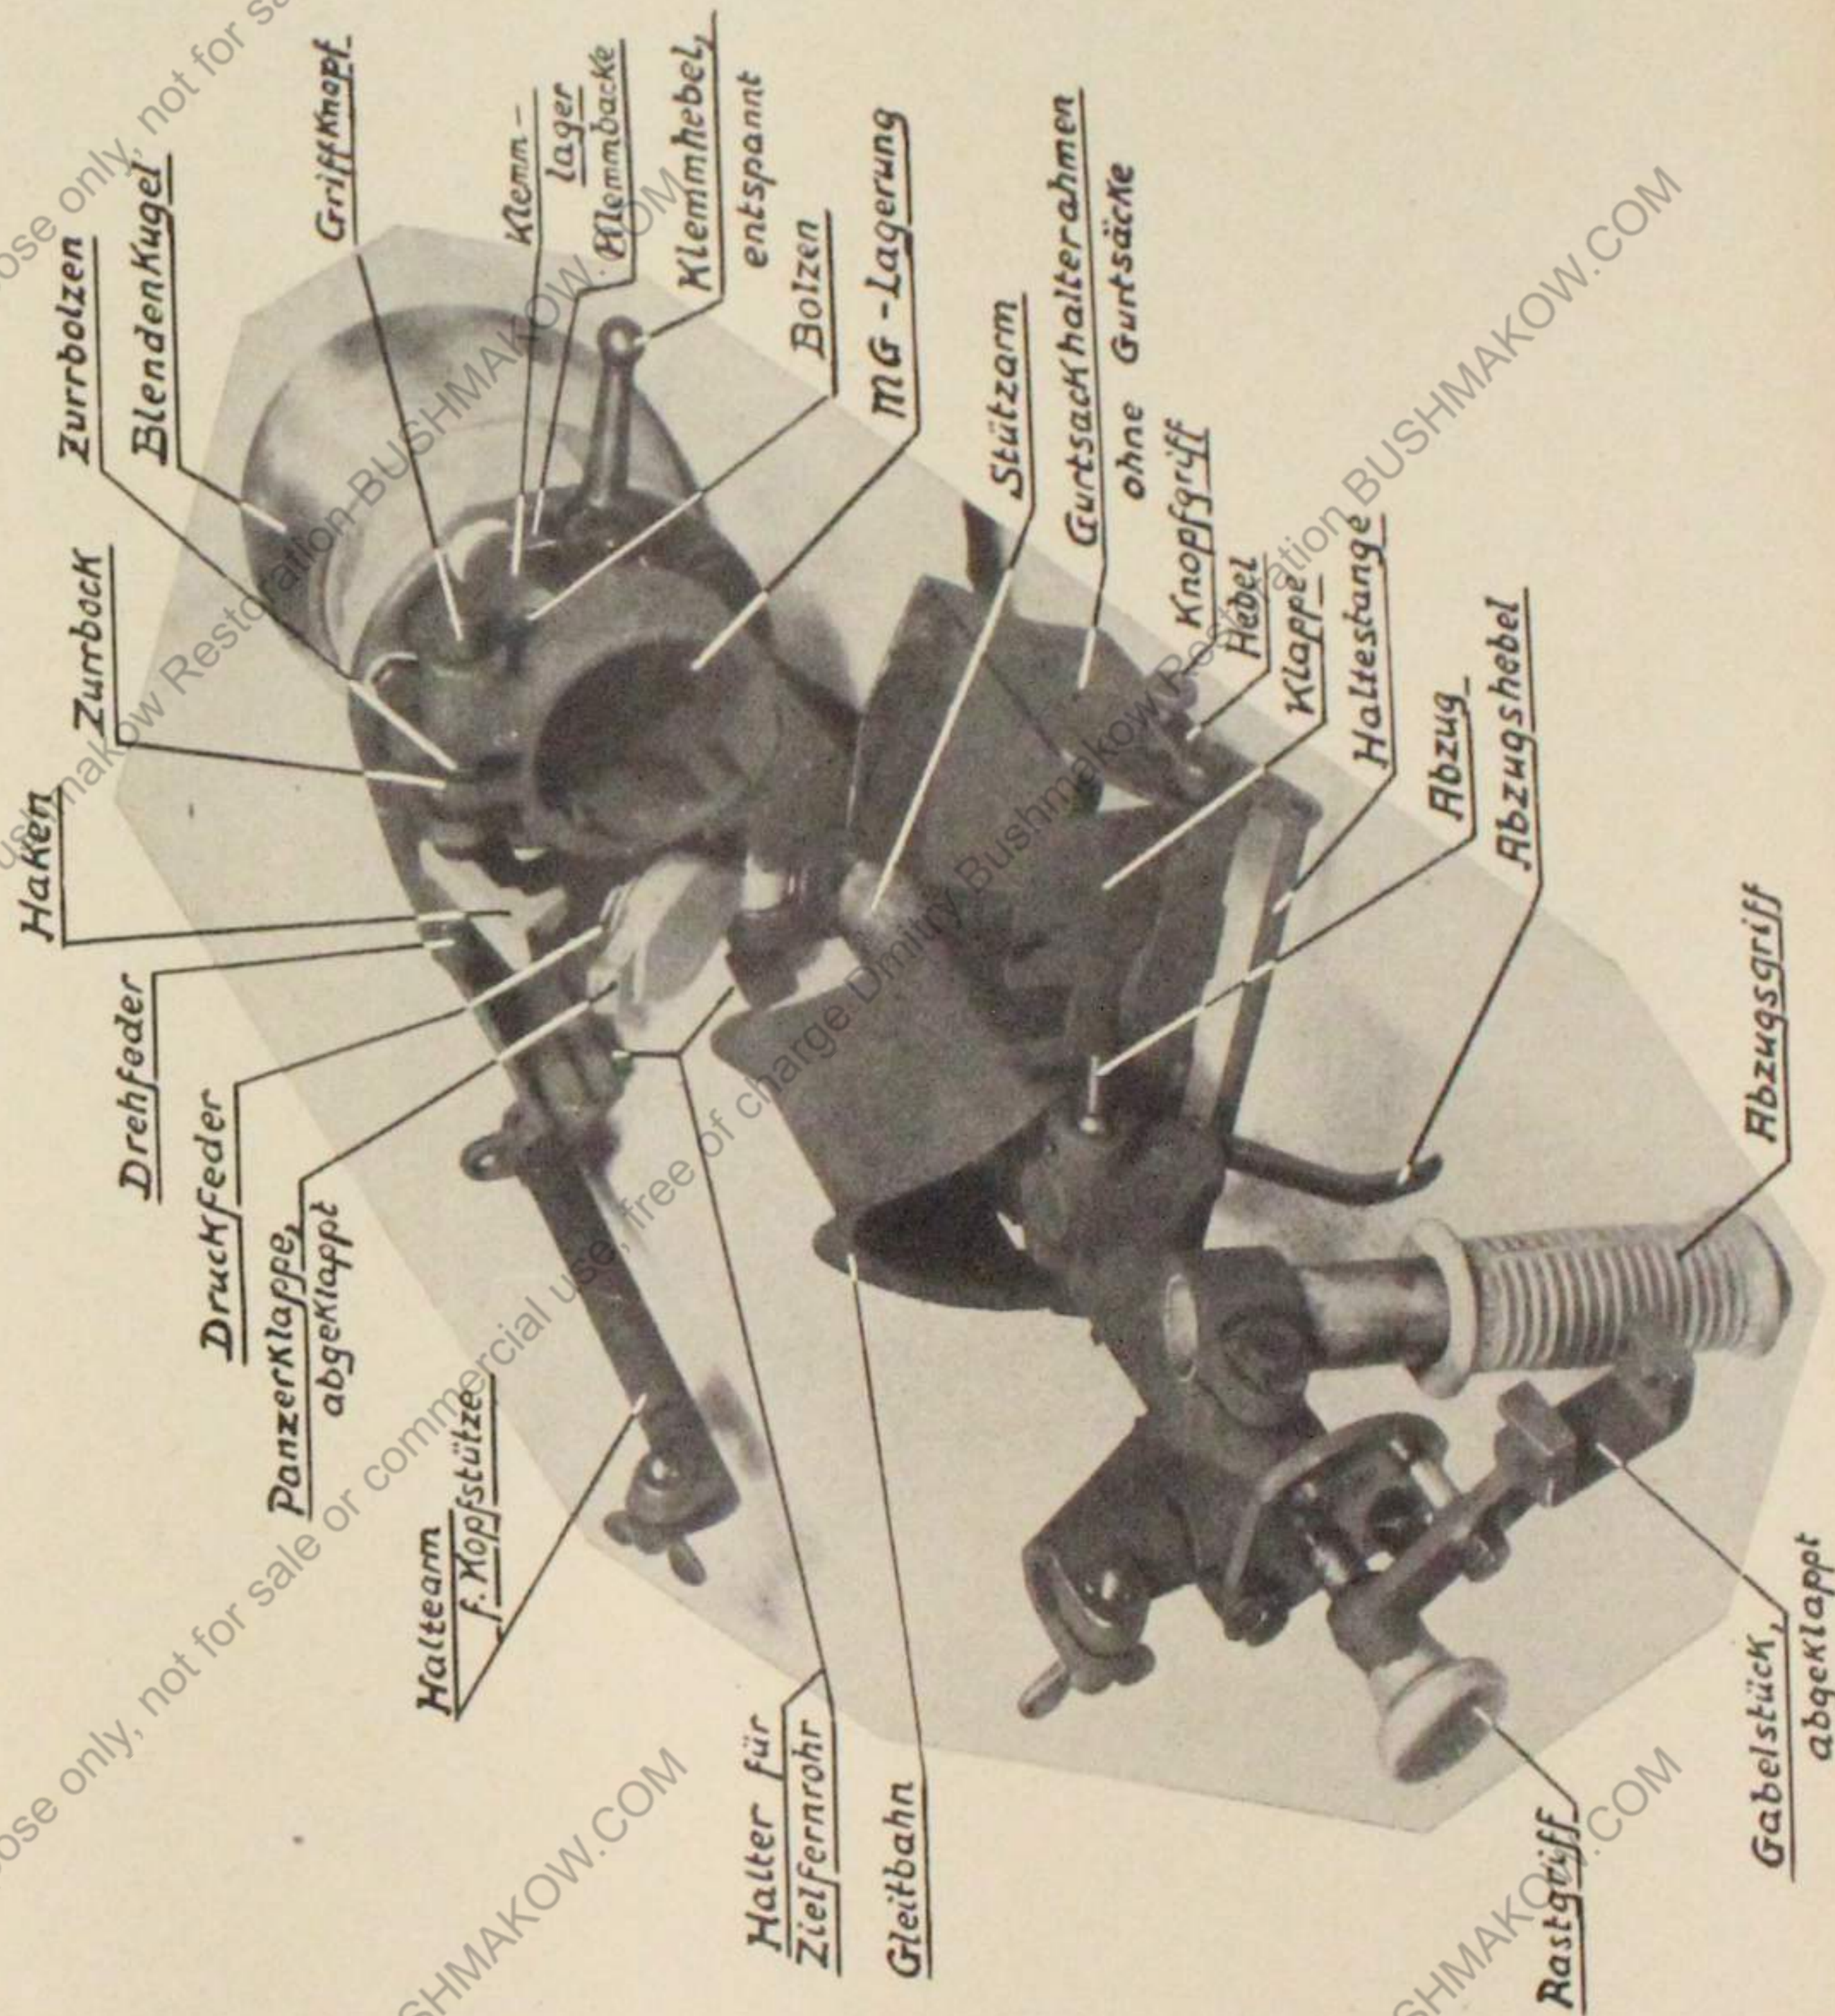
Kugelblende 50, ohne Optil, ohne MG, Innenaussicht von rechts
